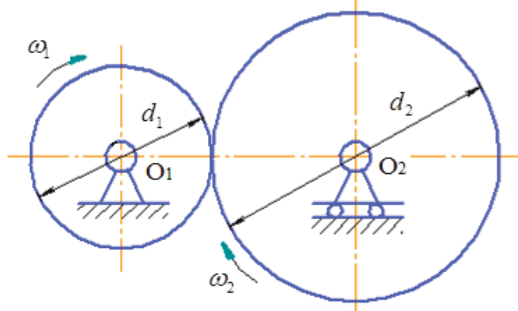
Кінематична схема фрикційної передачі з циліндричними котками
